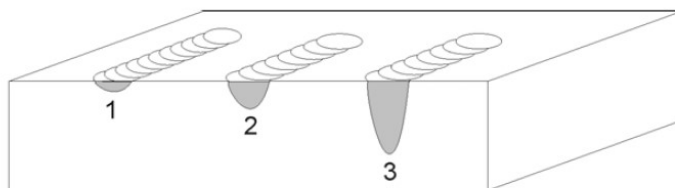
Tipos de soldadura; 1 condução, 2 condução/penetração, 3 penetração ou *keyhole* [19]
